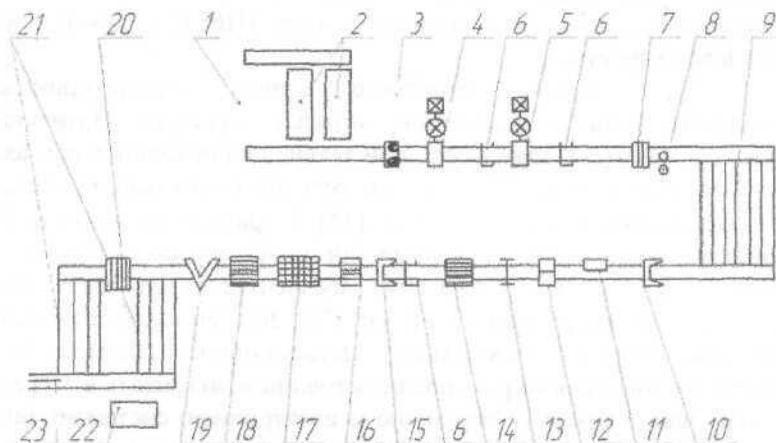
Схема розташування основного обладнання стану 5500 заводу у Міндзусімі: 1-склад слабів; 2-нагрівальні печі; 3-окалиноламач; 4-чорнова кліт; 5-чистова кліт; 6-товщиномір; 7-машина гарячої правки; 8-пристрій для маркіровки; 9-холодильник; 10-ножиці для відрізання кінців; 11-пристрій для клеймування зразків; 12-пристрій для маркіровки; 13-ножиці для відрізання кромок; 14-агрегат поздовжнього різання; 15-ножиці для відрізання кінців; 16-пристрій для клеймування готових листів; 17-інспекторський стіл; 18-машина для наклеювання ярликів; 19-листоукладальник; 20-листоправильна машина холодної правки;; 21-шлеперна решітка; 22-ультразвуковий дефектоскоп; 23-склад готової продукції.
